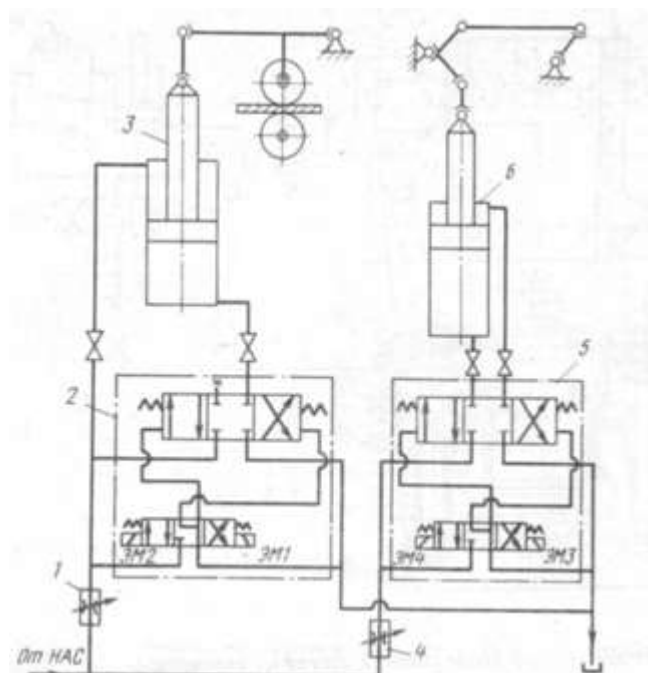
схема гидравлическая верхнего ролика тянущеправильной машины и поворотного лотка машин непрерывного литья заготовок
